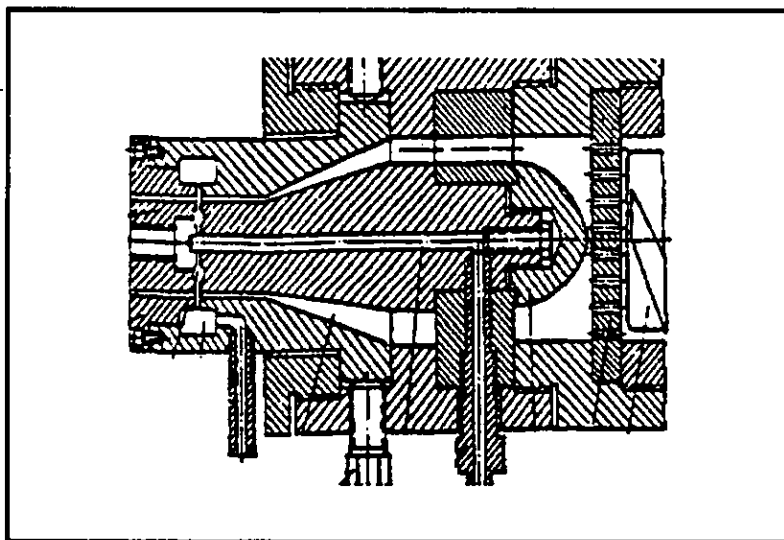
Cabezal perfilador para extrusionar tubos de tres capas.(18)
